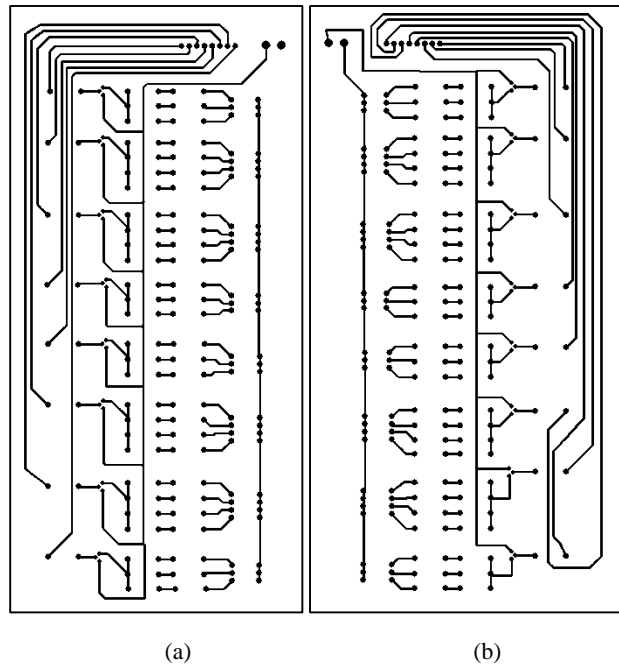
PCB del control de los LED: (a) control de la parte izquierda y (b) control de la parte derecha
